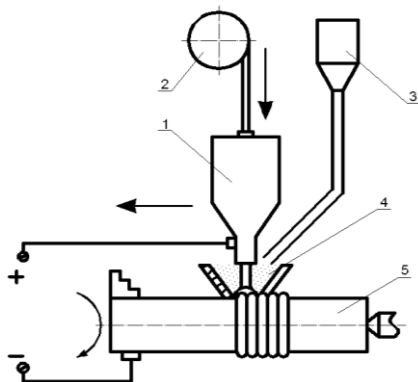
Схема установки для автоматической наплавки под слоем флюса:
